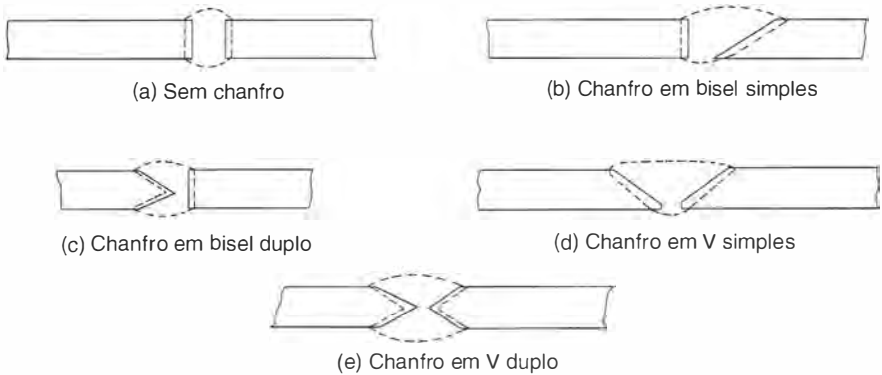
Tipos de solda de entalhe com penetração total.
